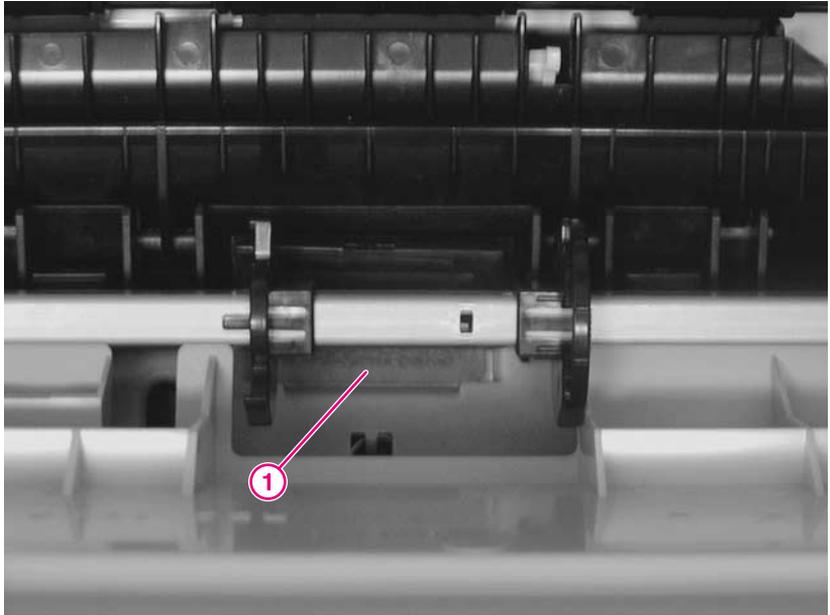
Entfernen des Trennstegs für Fach 1 (Innenansicht des Druckers, Draufsicht)
